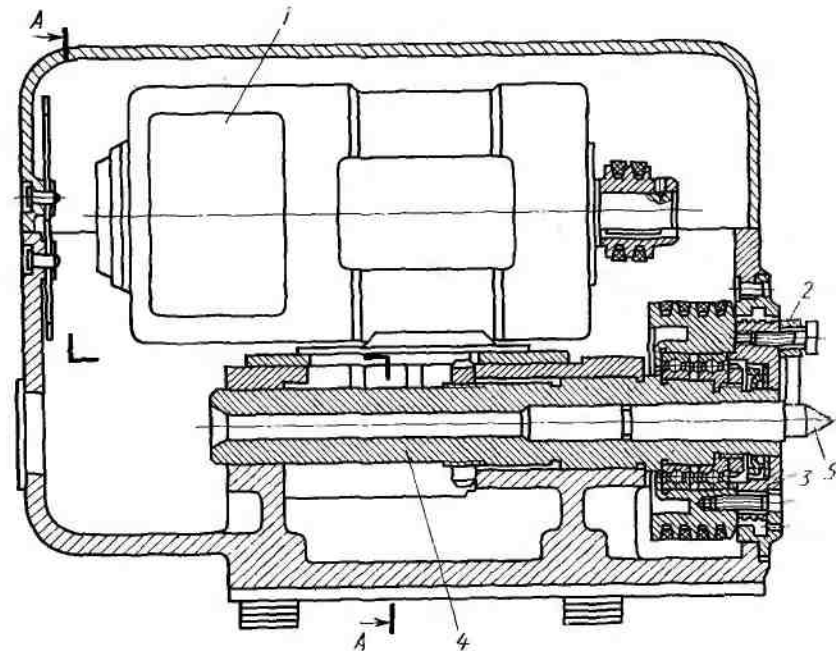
Конструкция передней бабки круглошлифовального станка
